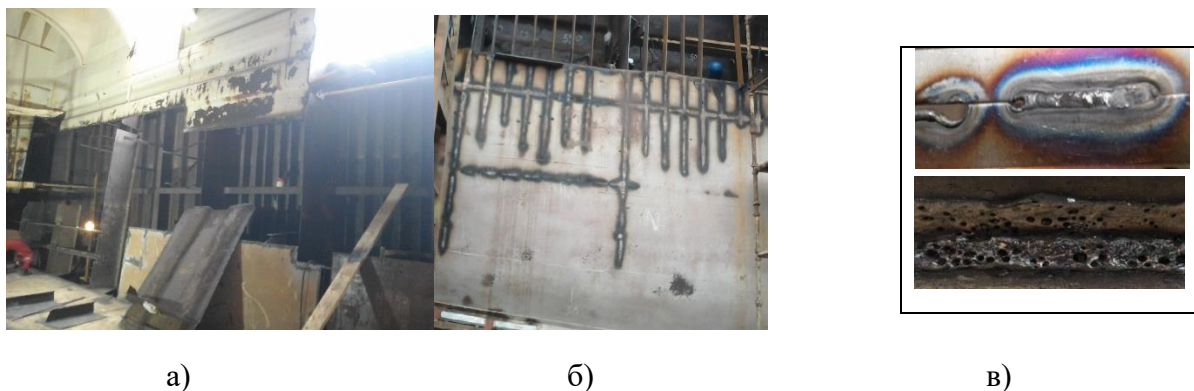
Ремонт с заменой двойного борта на танкере проекта 16776 СРЗ им. Бибиейбат: а – резка дефектных пластин переборки и установка новых их на втором борту, б- прожог металла корпуса судна при сварки бортового набора к обшивке, в-прожоги.
